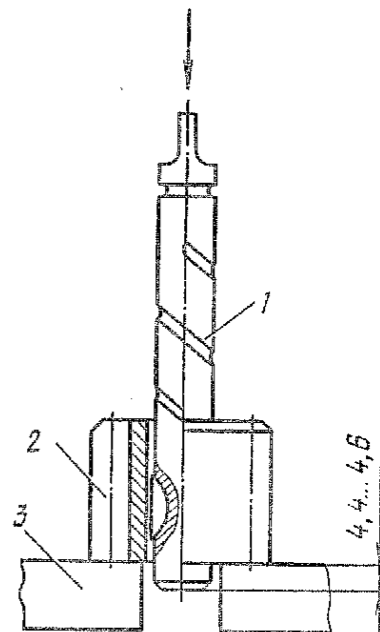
Напрессовка ведущей шестерни на валик масляного насоса:
